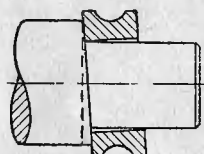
Положение кольца подшипника при заплечике, не перпендикулярном оси вала.
